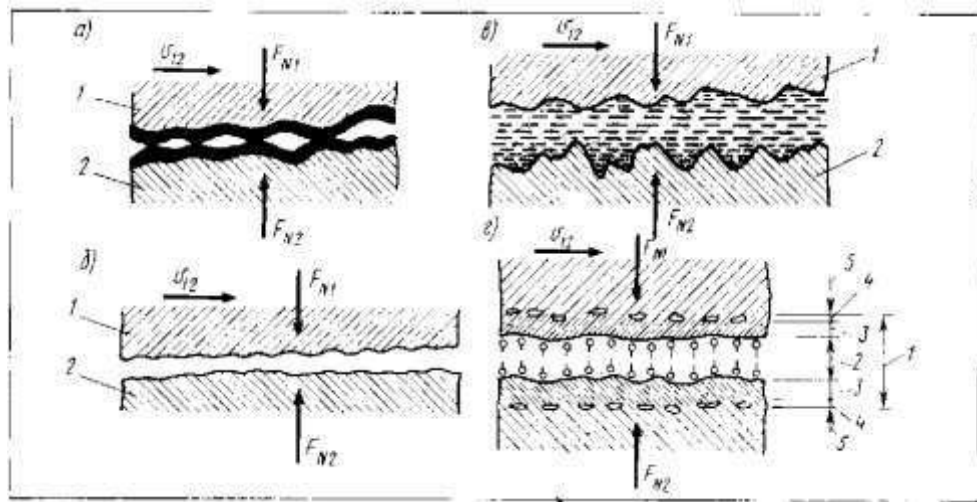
Види змащення поверхонь під час тертя деталей
